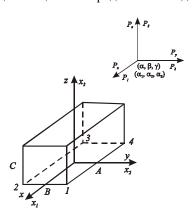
Действие усилий резания на приспособление, закрепленное в точках 1-4
